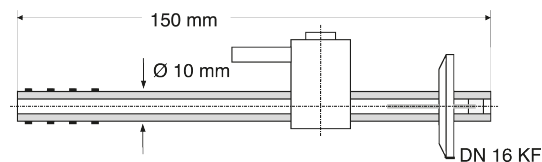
Prüfleck mit Stiftgehäuse und Schlauchstutzen
